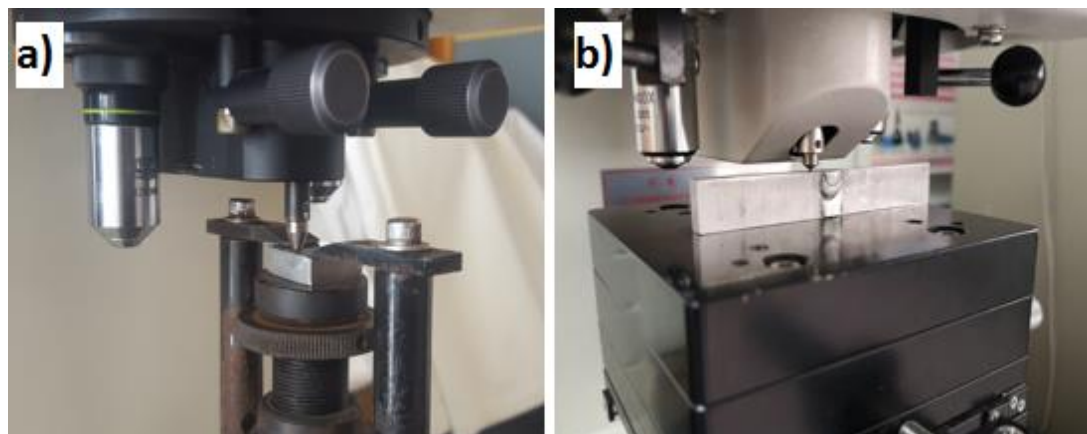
Ensayo de microdureza (a) Material Base (b) Probetas soldadas.
